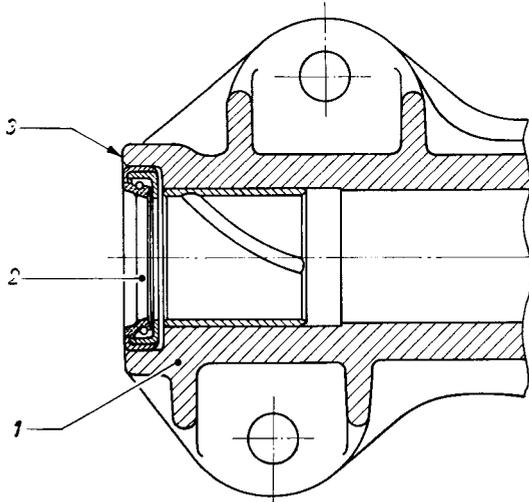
Öldichtring für Lenkstockwelle im Lenkgehäusehals
